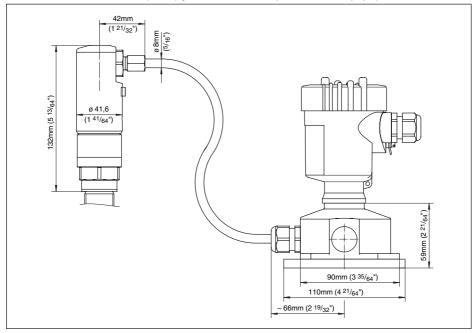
Carcasa del sensor - metal (IP 68) (10 bar) y carcasa externa (carcasa del equipo)
